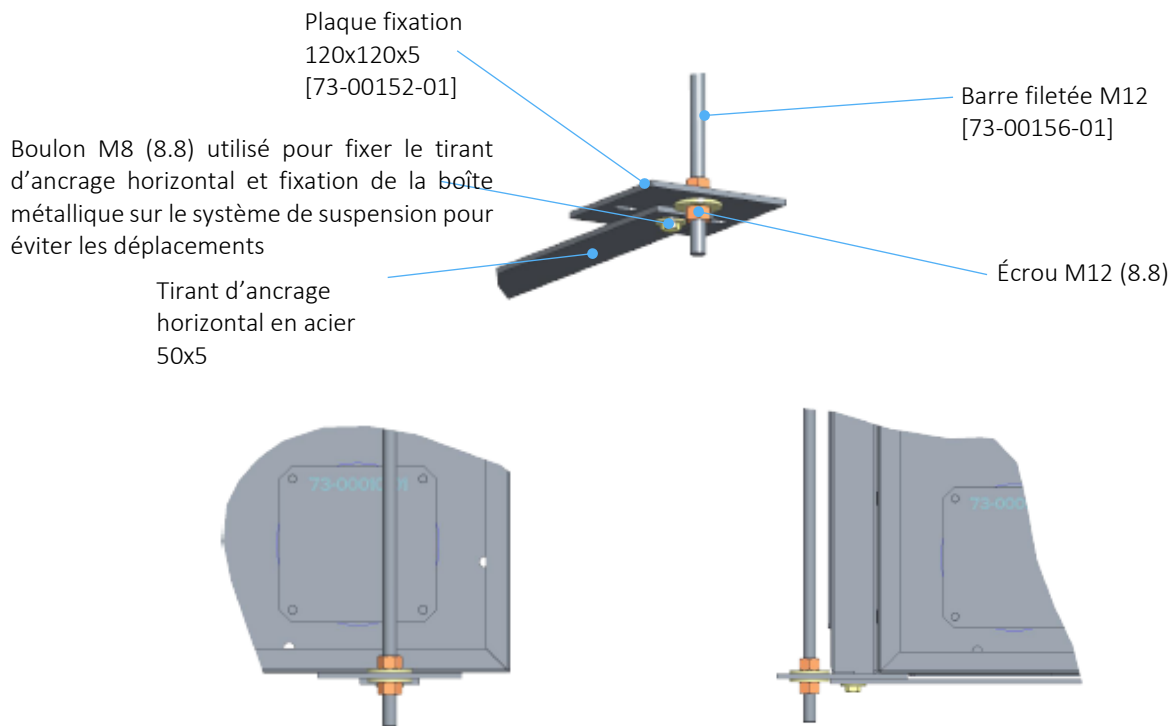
Système d'ancrage : fixation plaques sur la dark-box
